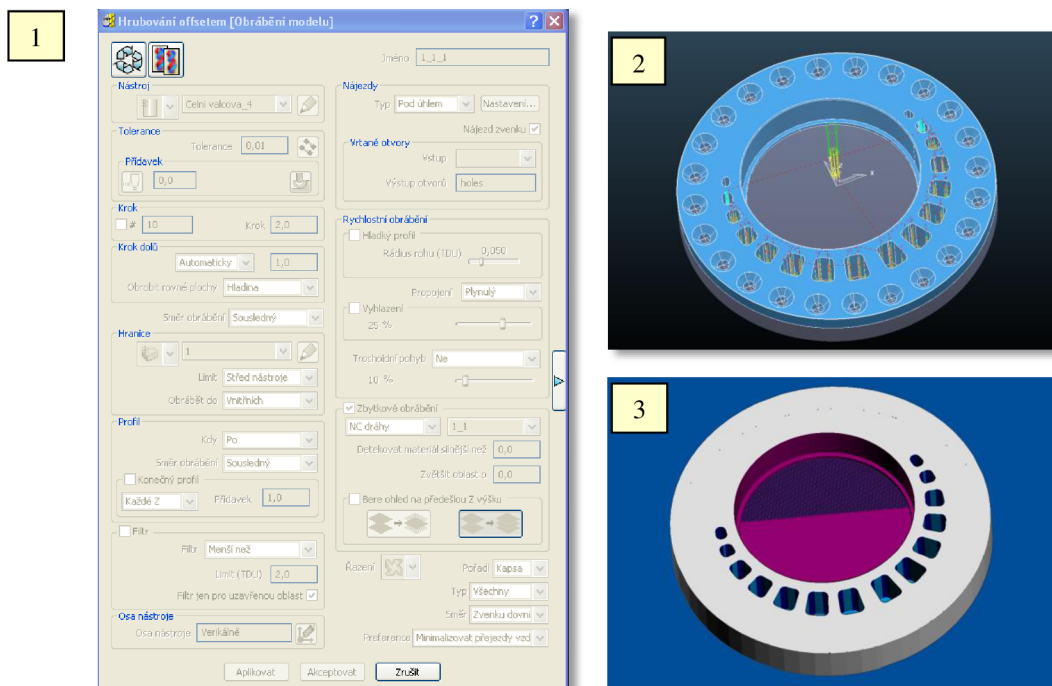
Hrubování offsetem – zbytkové obrábění:
